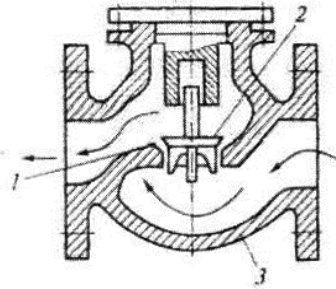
Зворотний клапан: 1 – сідло; 2 – клапан; 3 – корпус
